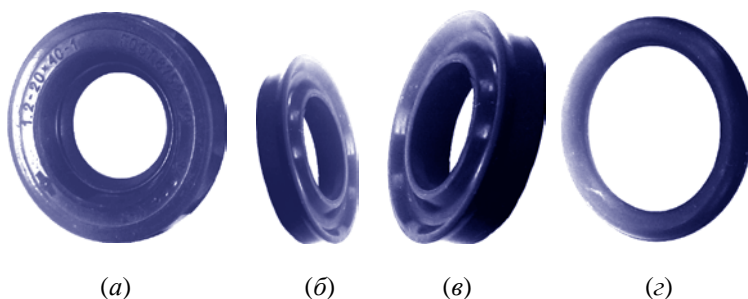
Внешний вид конструкции уплотнительных РТИ кольцевой формы
